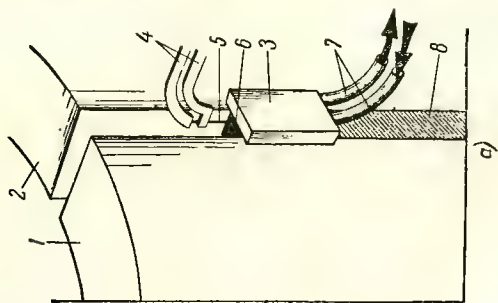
Электрошлаковая сварка продольного шва обечайки котельного барабана.
